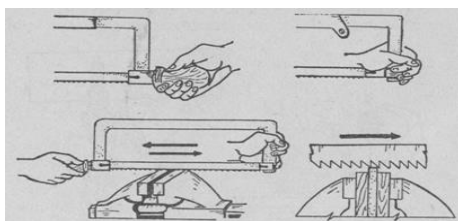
Приемы работы с ножовкой по металлу и слесарными ножницами
